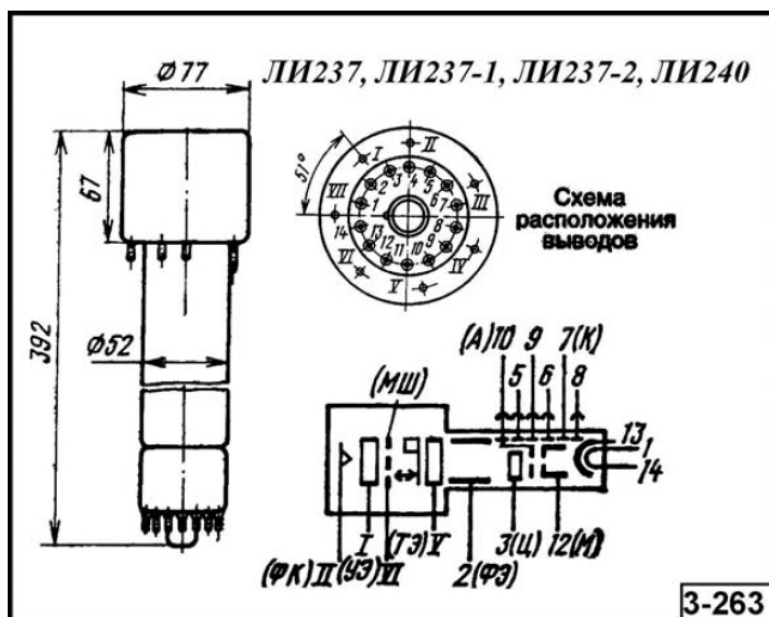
Внешний вид, габаритные размеры и назначение выводов суперортиконов
